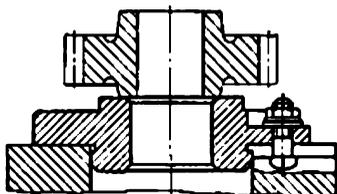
Самоустанавливающая опора для протягивания отверстия при необработанном торце заготовки
